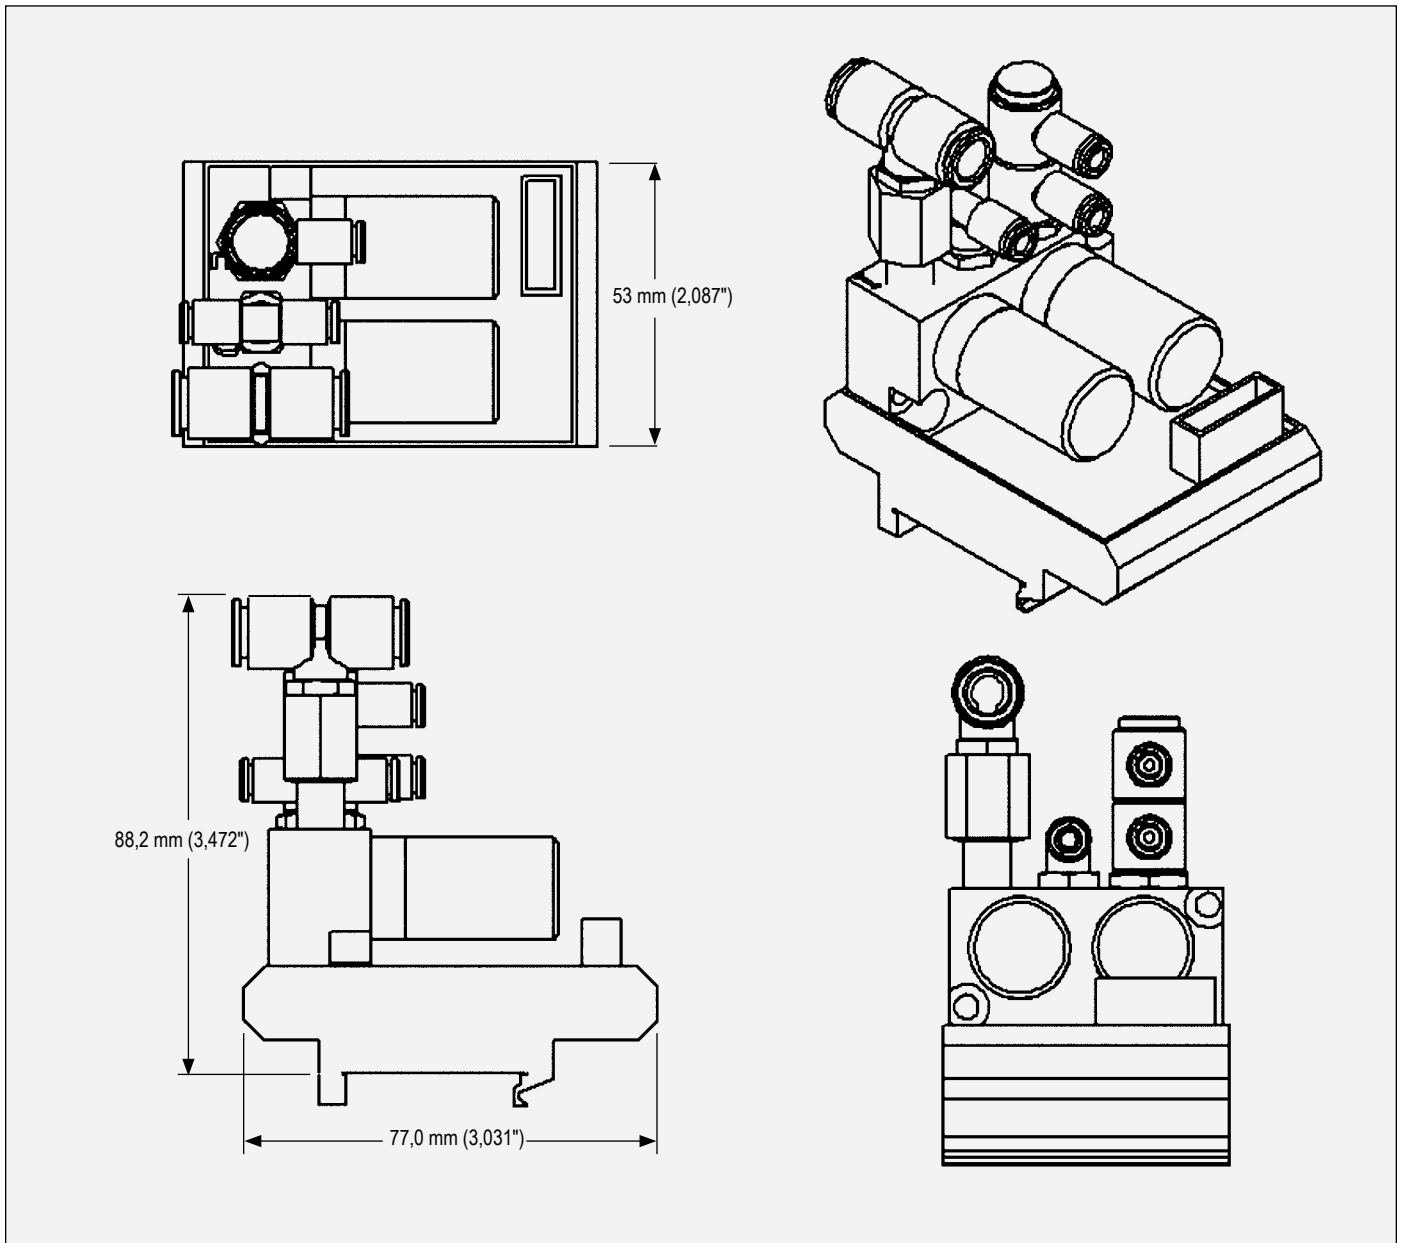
Dimensions de fixation E-vers-P sur rail DIN
